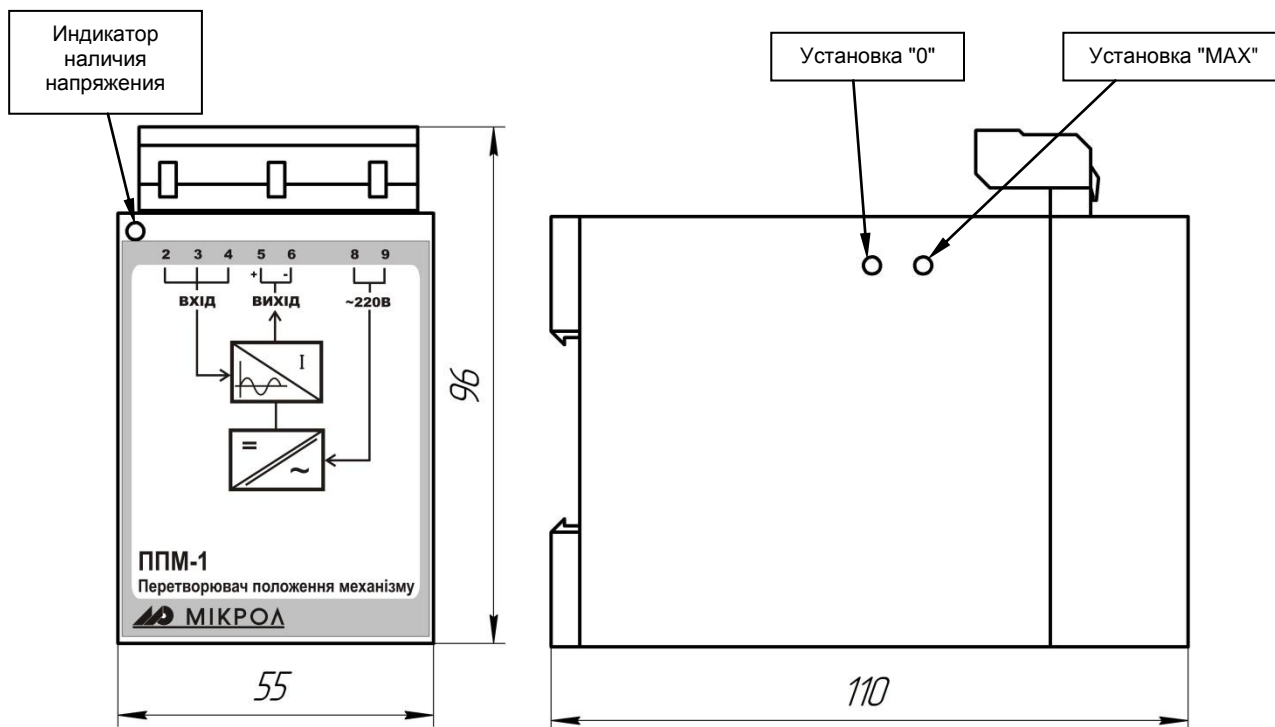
Внешний вид и габаритные размеры ППМ-1
